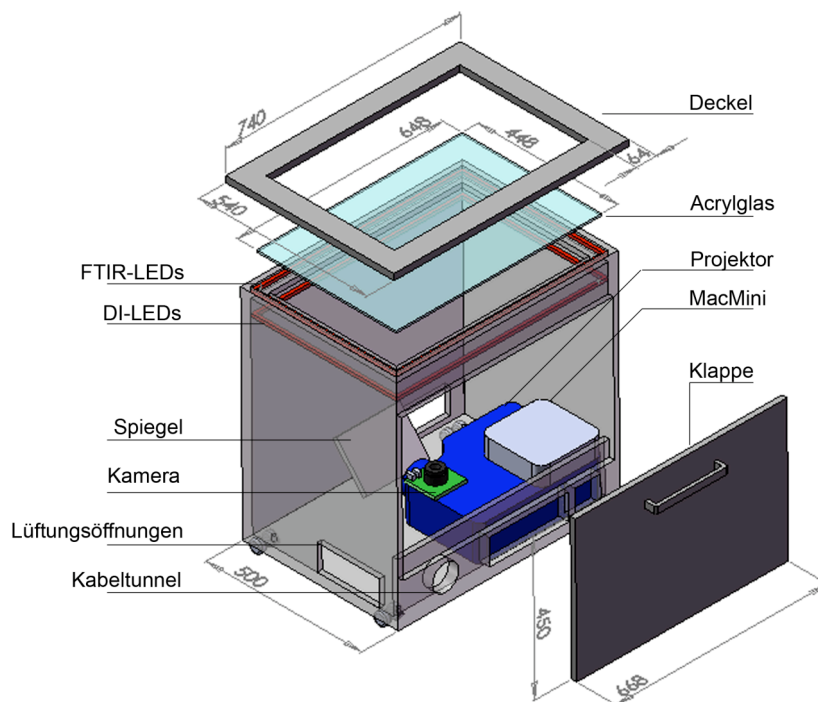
CAD-Zeichnung des Virtable mit Vermaßung in mm.
